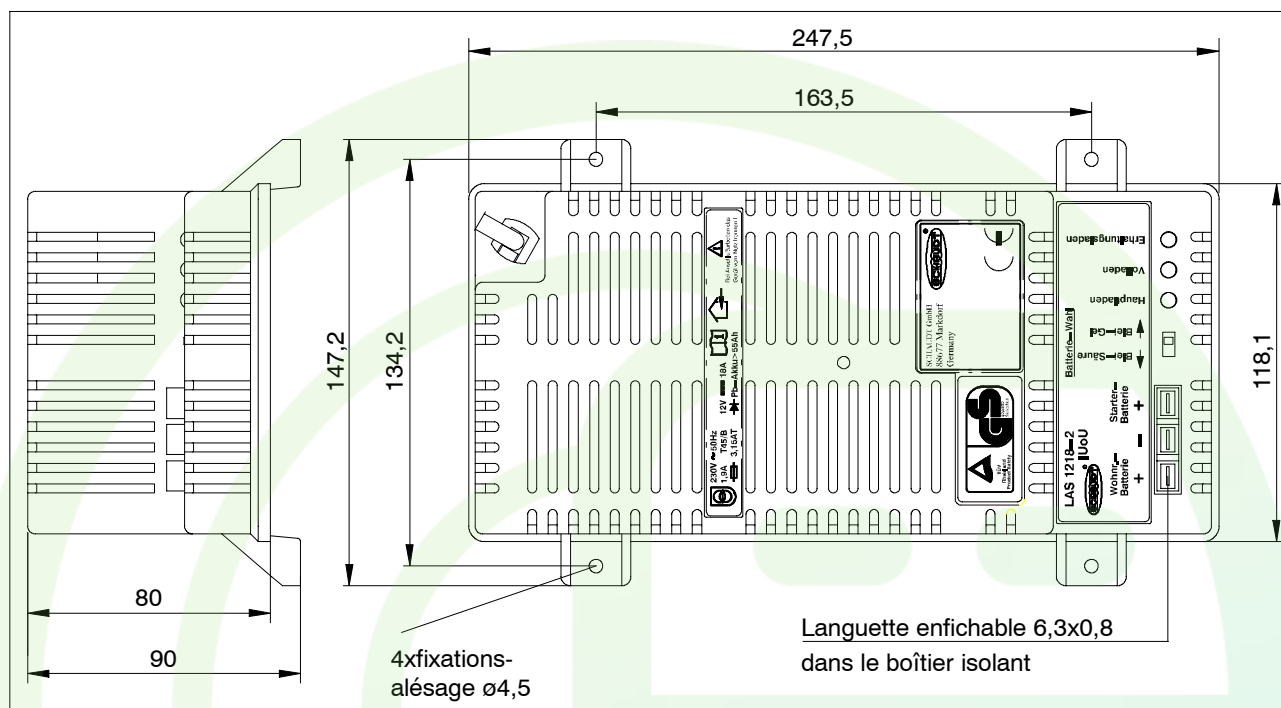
Plan coté du chargeur de batterie LAS 1218-2 (dimensions en mm)
